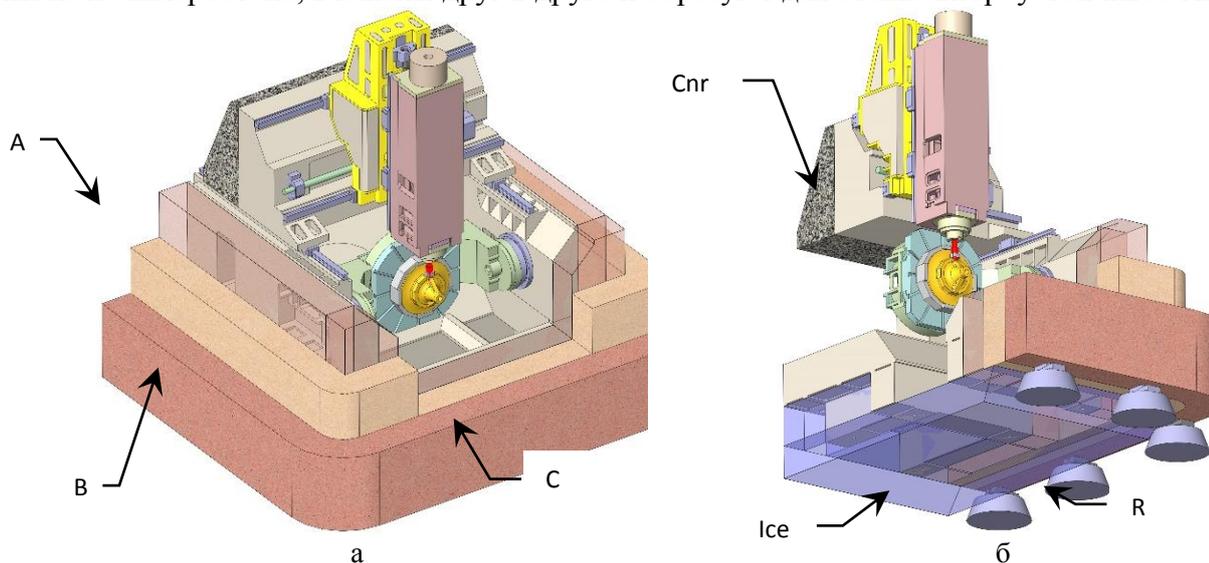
Конверт-усиление станка полимербетоном в случае исполнения НС без большинства чугунных деталей: а – вид сверху; б – вид снизу в разрезе
